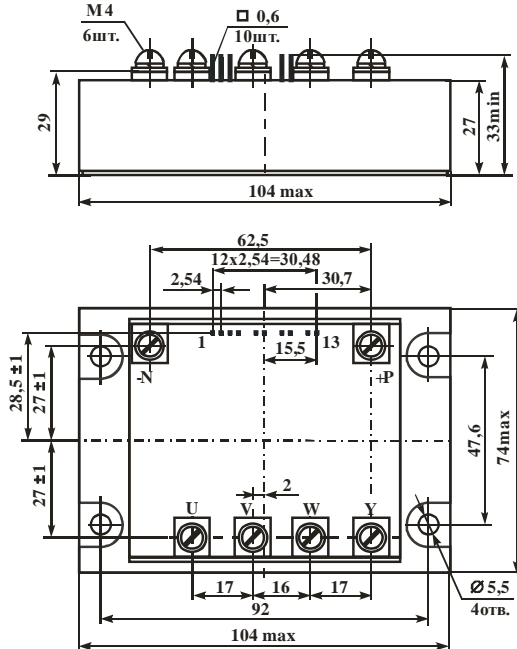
Габаритный чертеж модуля M13B-30-12; M13B-50-12
